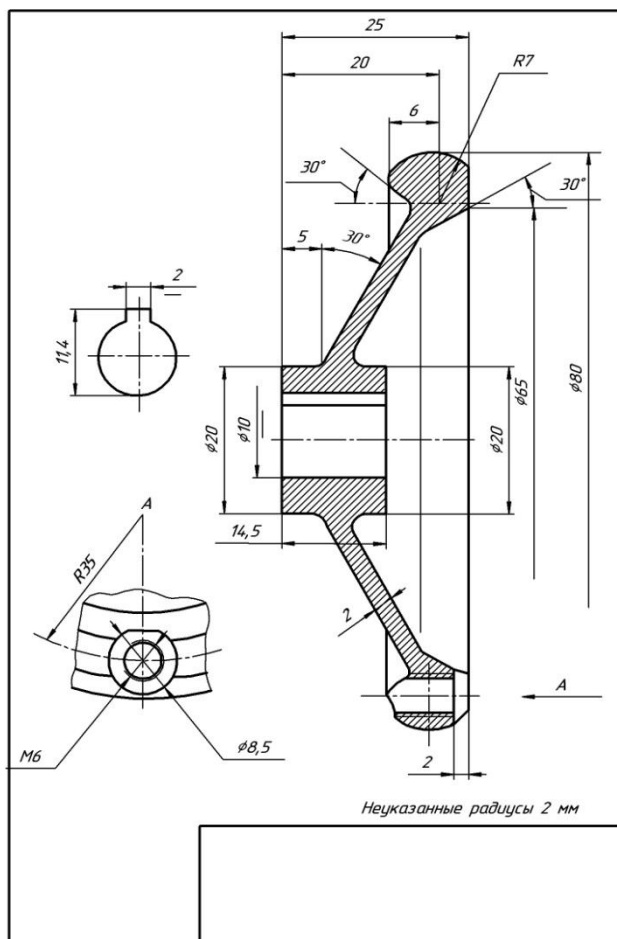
Пример выполнения рабочего чертежа детали
